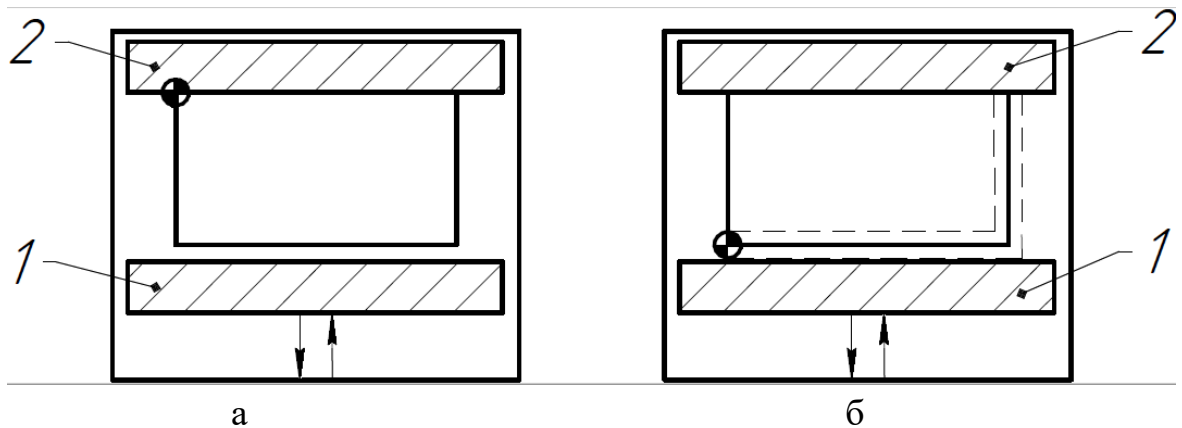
Два варіанти розташування нульової точки деталі в лещатах: а) нерухома губка - 2; б) рухома губка - 1, що виконує затиск заготовки.
